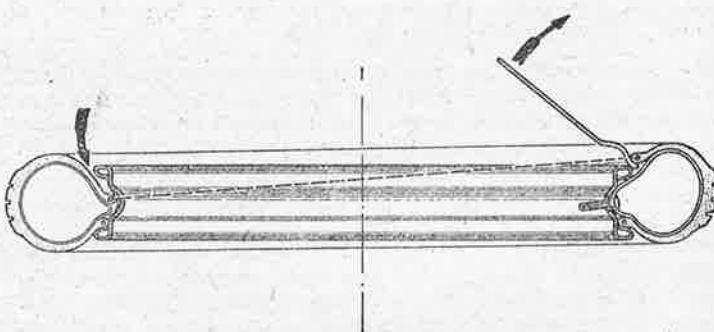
Обод и шина в разрезе - монтаж покрышки
